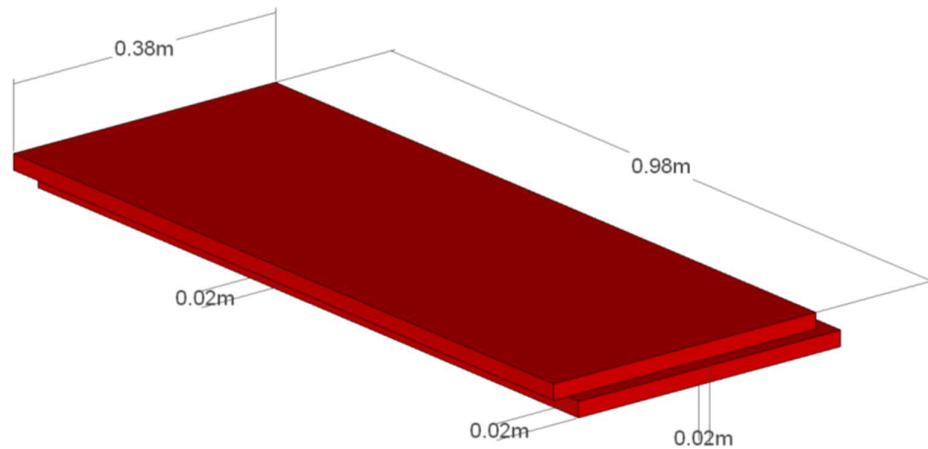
Configuración geométrica de plancha - Parte No.1 del proyecto.
